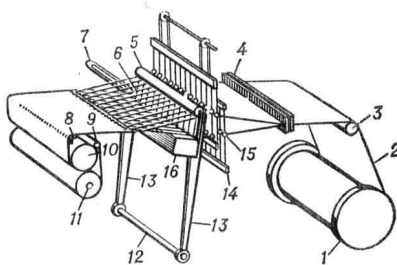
Принципиальная схема образования ткани на ткацком станке: 1 — навои; 2 — нити основы; 3 — скало; 4 — ламели; 5 — вершник; 6 — бёрдо; 7 — челнок; 8 — грудница; 9 — направляющий валик; 10 — вальня; 11 — товарный валик; 12 — подбанный вал; 13 — лопасть батана; 14 — ремизка; 15 — глазок галев; 16 — батан.
